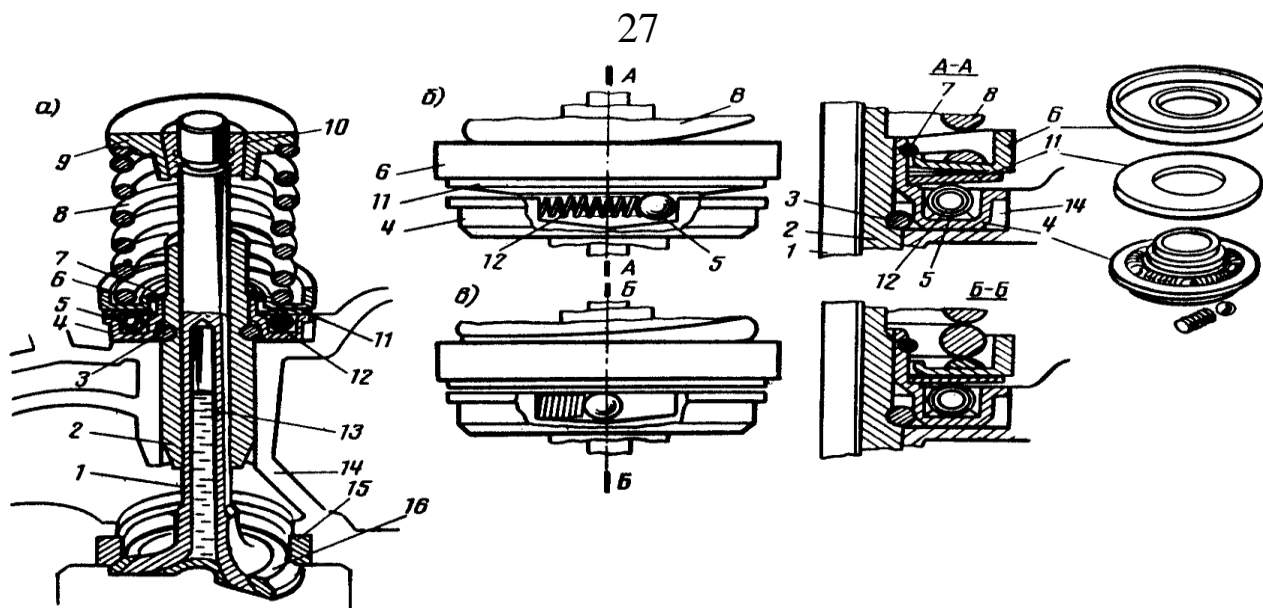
Выпускной клапан двигателя автомобиля ЗиЛ-431410: 1 – стержень; 2 – направляющая втулка; 3 и 7 – замочные кольца; 4 – корпус; 5 – шарики; 6 – шайба; 8 – пружина; 9 – тарелка; 10 – конические сухарики; 11 – дисковая пружина; 12 – возвратные пружины; 13 – охладитель (металлический натрий); 14 – головка цилиндров; 15 – вставки из жаропрочного чугуна; 16 – головка клапана
